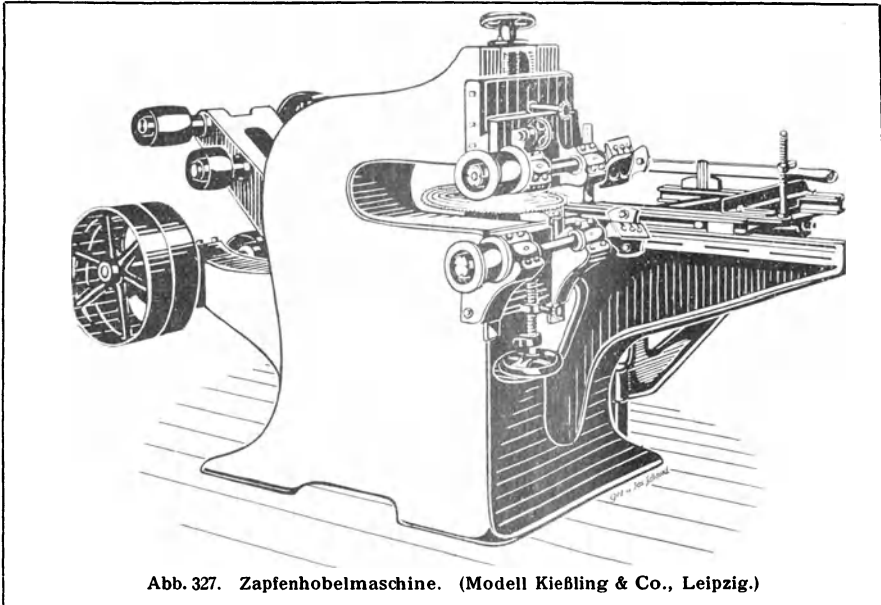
Zapfenhobelmaschine. (Modell Kiebling & Co., Leipzig.)
